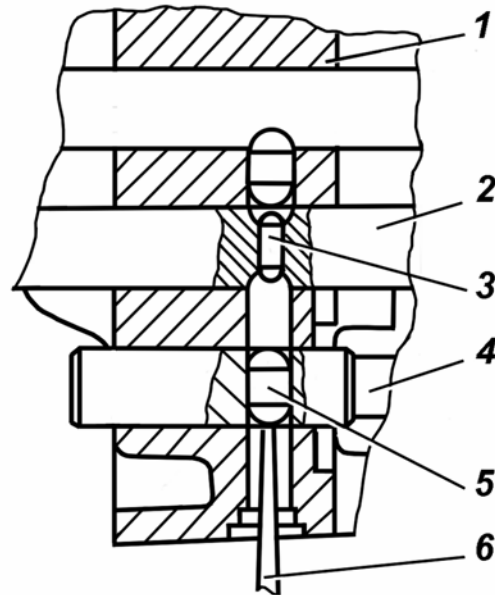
Установка стопорного плунжера: 1 – шток; 2 – стопорный палец; 3 – оправка; 4 – задний картер; 5 – бородок; 6 – стопорный плунжер
